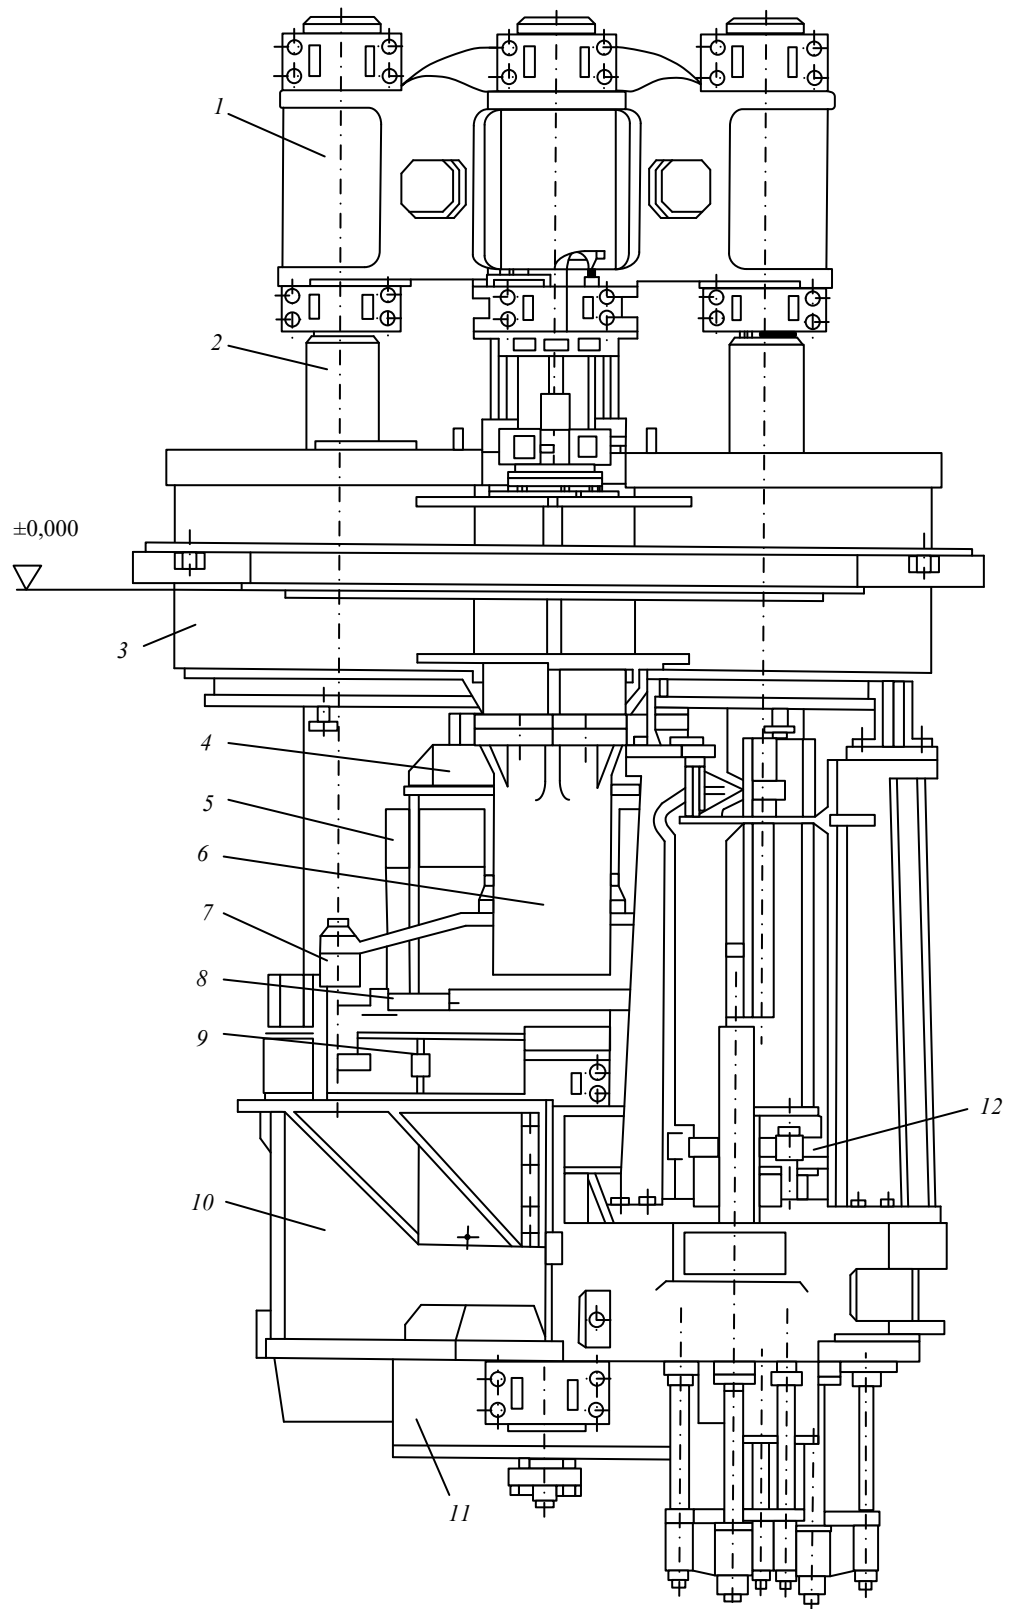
Вертикальний прес з поворотним столом: 1 – верхня траверза; 2 – колонна; 3 – поворотний стіл; 4 – поперечини; 5 – поперечний циліндр підйому матриці; 6 – опорна втулка; 7 – зубчасте колесо; 8 – шестерня; 9 – редуктор; 10 – нижня траверза; 11 – головний циліндр; 12 – виштовхувач
